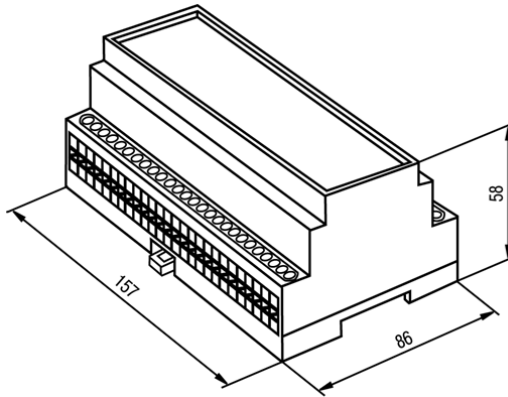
Габаритный чертёж корпуса для крепления на DIN-рейку 35 мм
